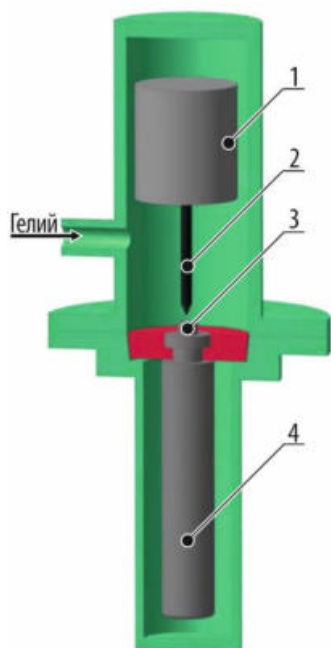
Схема установки сварки в среде повышенного давления: 1 — камера; 2 — электрод; 3 — сварной шов; 4 — изделие
